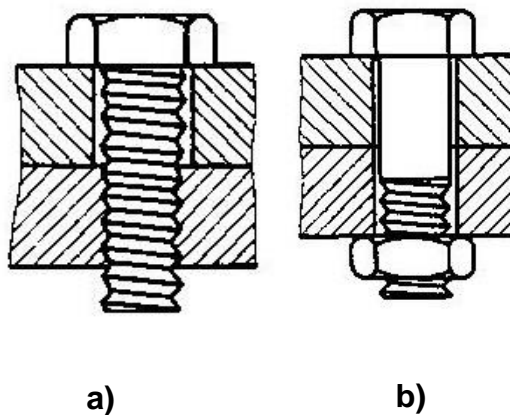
a) Unión tornillo-agujero roscado b) Unión tornillo-tuerca
